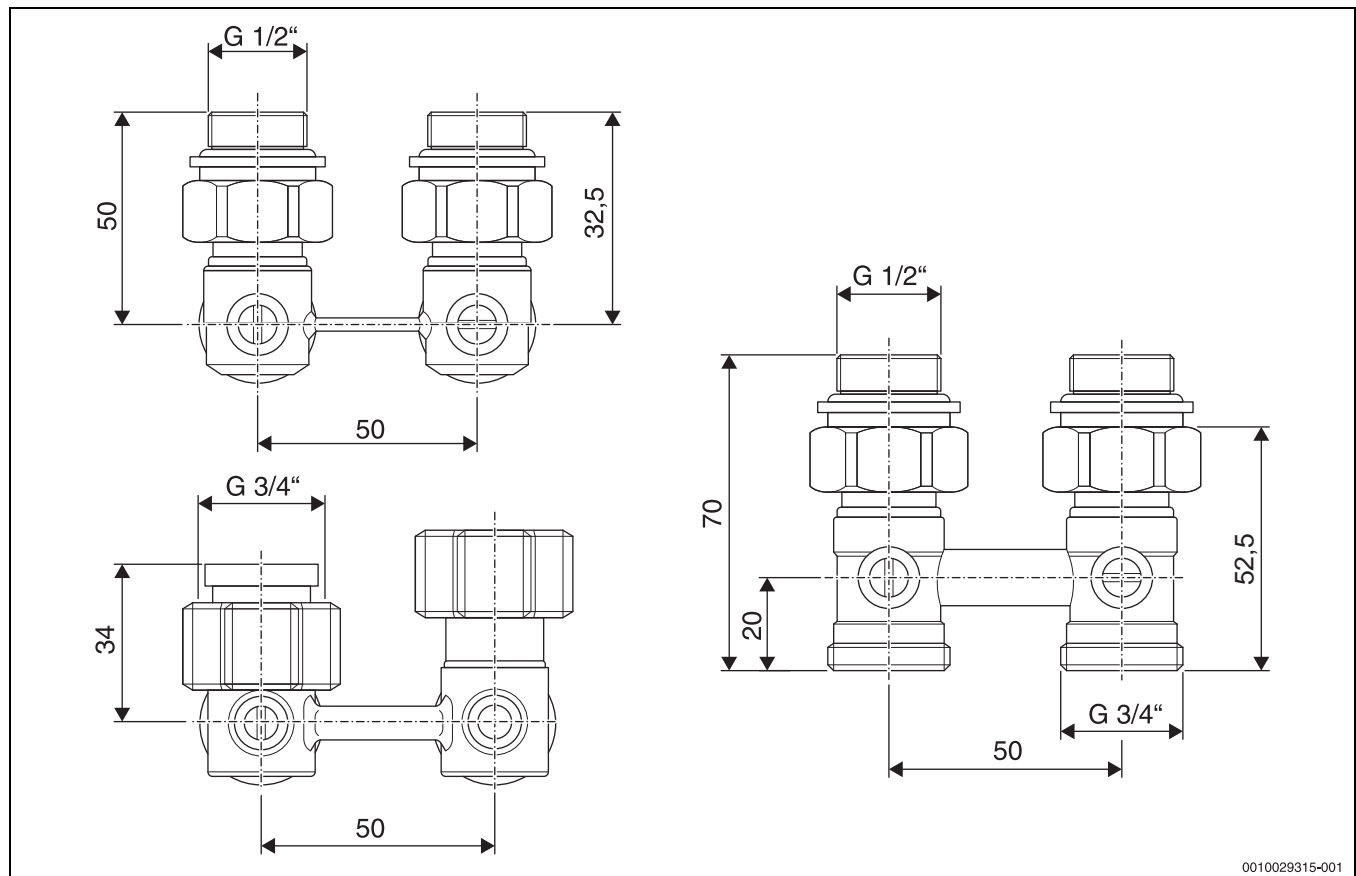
Baumaße Logafix H-Block (Maße in mm)
